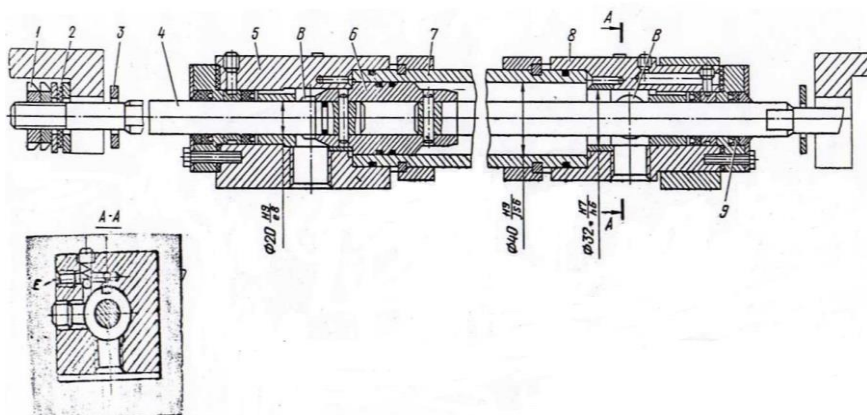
Гидроцилиндр станка мод. 3Е711В
